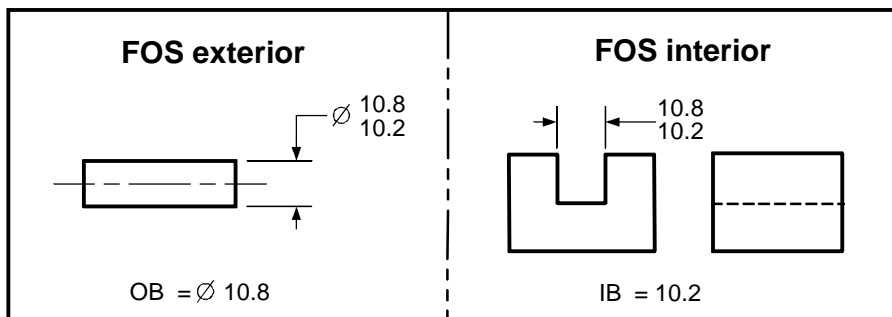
Frontera de peor caso si no hay tolerancia geométrica especificada
